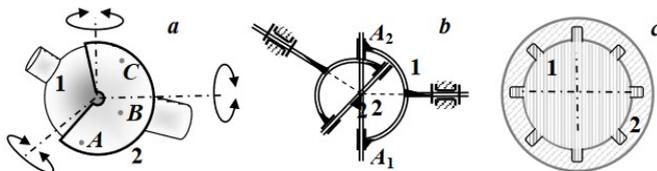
Кинематические пары с элементарными (а) и разделительными (b, c) избыточными связями
